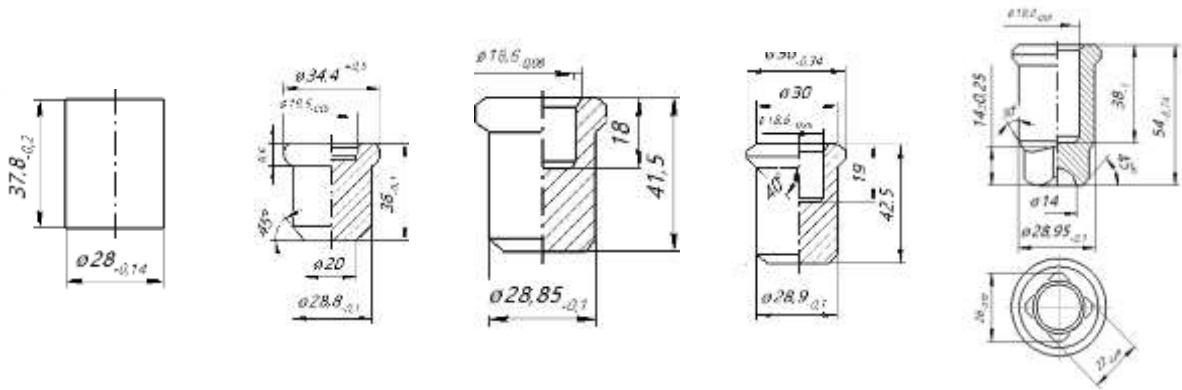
Переходи при штампуванні деталей складної форми
